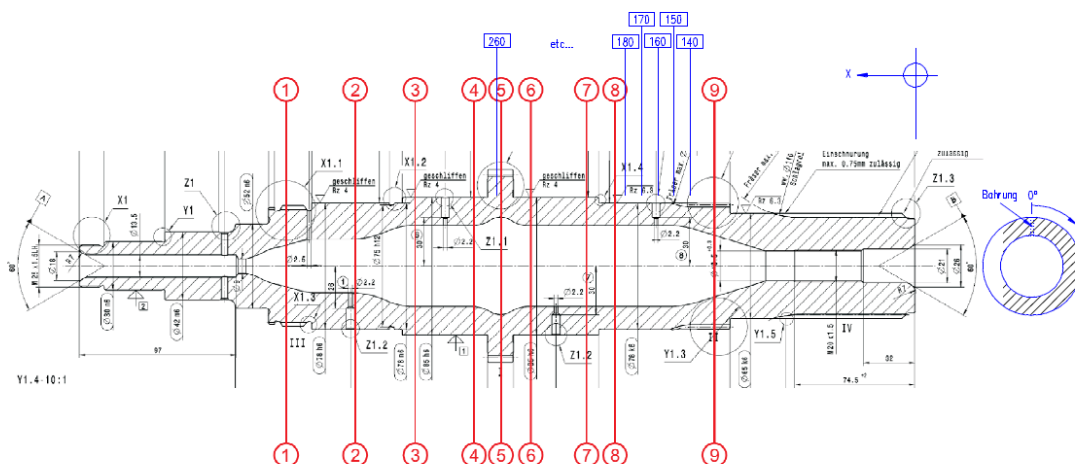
Ausgewählte Wellenabschnitte und Messebenen für die Wanddickenmessung
